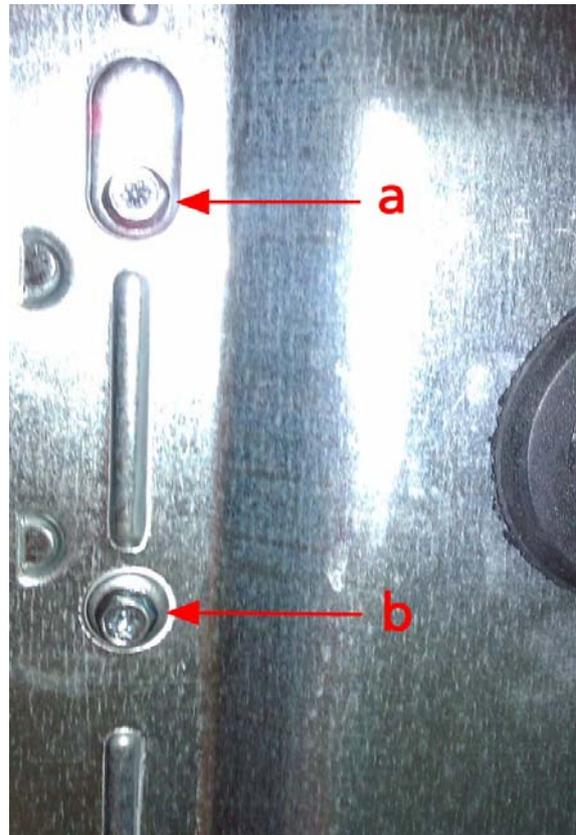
Befestigung des neuen Pumpensockels mit zwei Torx-Schrauben (a, b) von außen an der Gehäuserückwand. Links am Bildrand sind die Laschen des Sockels zu sehen.
